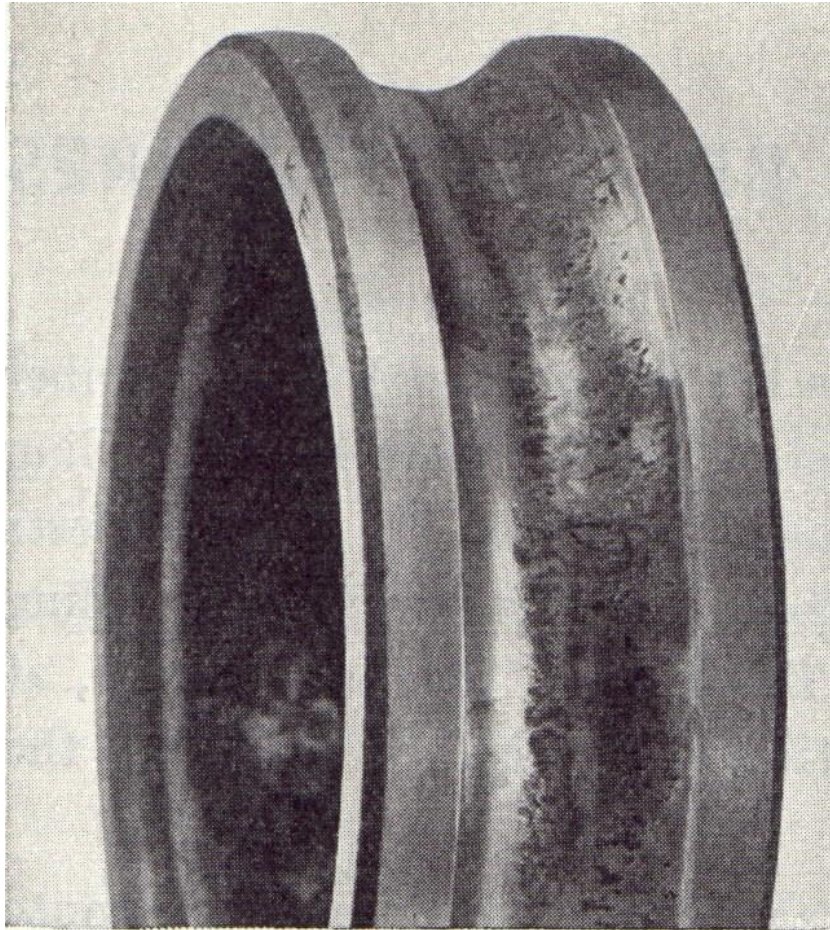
avería por exfoliación avanzada en el camino de rodadura del aro interno de un rodamiento de bolas [2].
